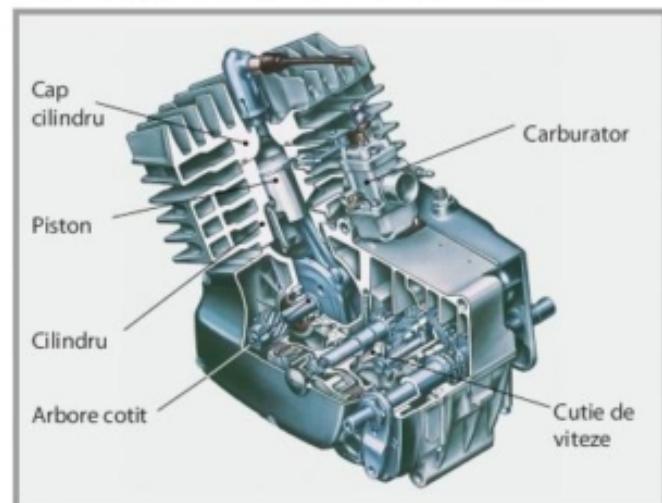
Motor pentru bicicletă motorizată cu cutie de viteze integrată
